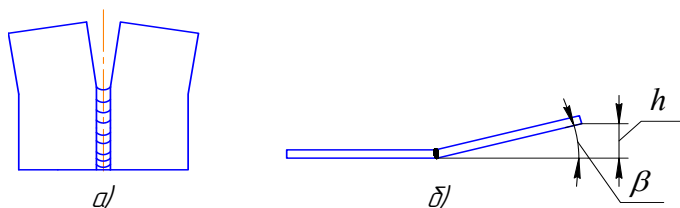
Различные виды сварочных деформаций (перемещения): *а* — в плоскости свариваемых пластин; *б* — угловой поворот пластин
